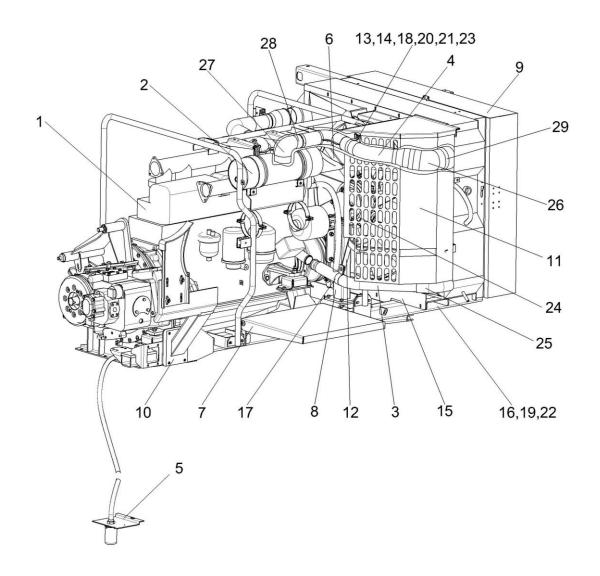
Установка двигателя Д260.7С-504 КЗК-10-1-0106000 (лист 1)
